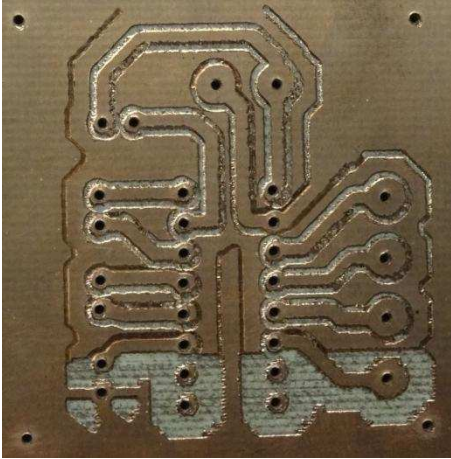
PCB con fresa cónica, broca fina, desbastado 20%
